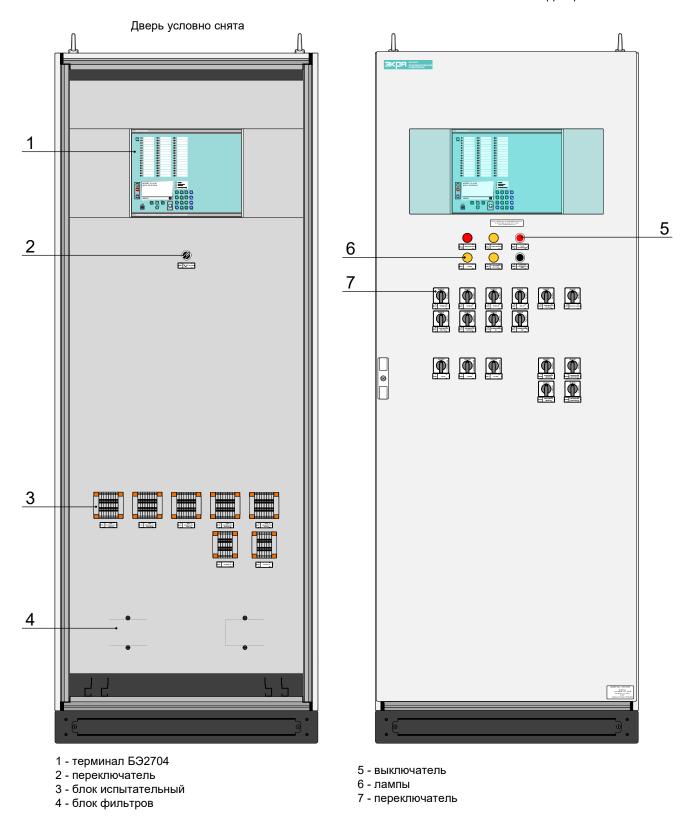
Общий вид шкафа типа ШЭ2607 042
